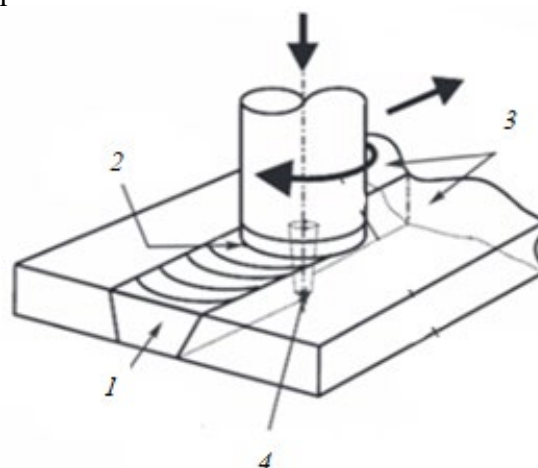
Схема сварки трения с перемешиванием:
